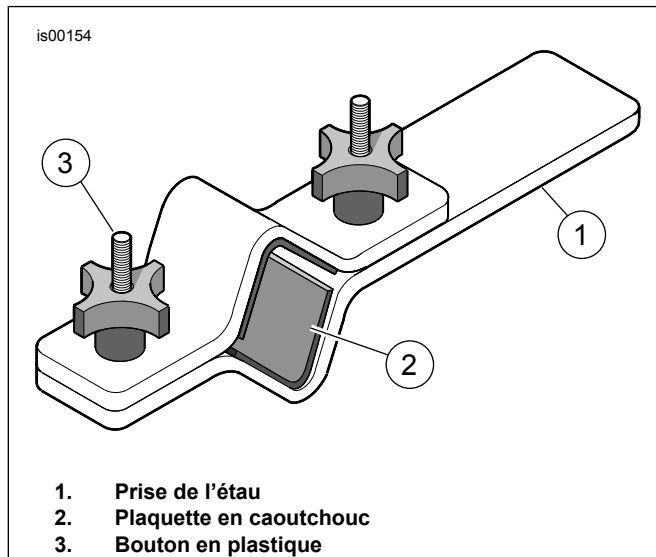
Fork Tube Holder (Support de tube de fourche) (HD-41177)
